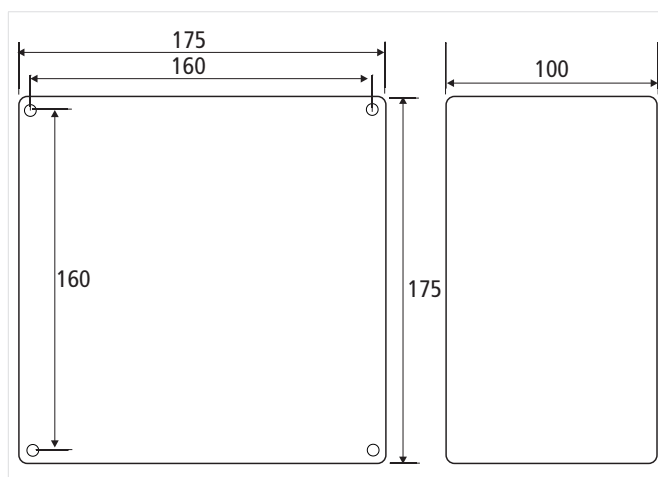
Maßbild Gehäuse GEH-HS (TP oder GS), Draufsicht und Seitenansicht
